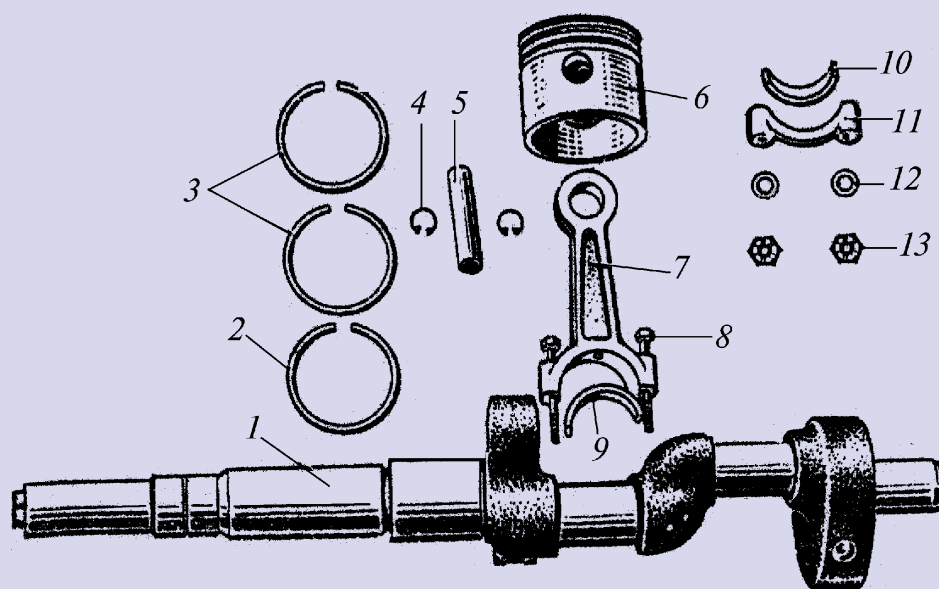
Коленчатый вал и шатунно-поршневая группа компрессора типа «V»: 1 — коленчатый вал; 2 — маслосъемное кольцо; 3 — компрессионные кольца; 4 — стопорная шайба; 5 — поршневой палец; 6 — поршень; 7 — Шатун; 8 — шатунный болт; 9 — верхний вкладыш; 10 — нижний вкладыш; 11 — нижняя головка шатуна; 12 — шайбы; 13 — гайки шатунных болтов
